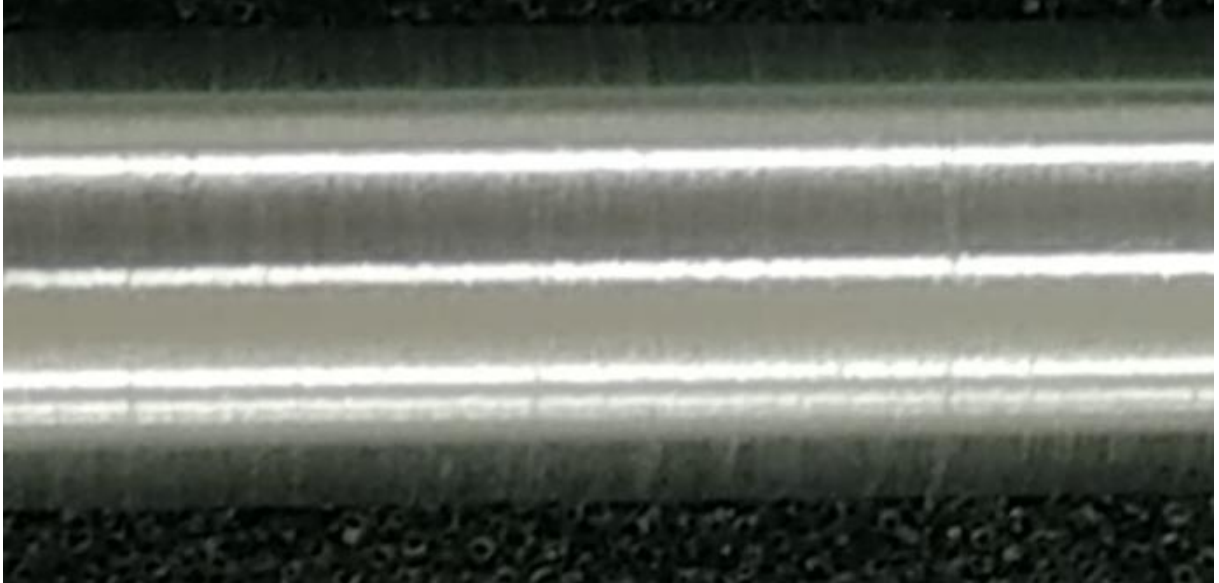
Imagem ampliada da superfície da peça usinada pela ferramenta de aço rápido.
